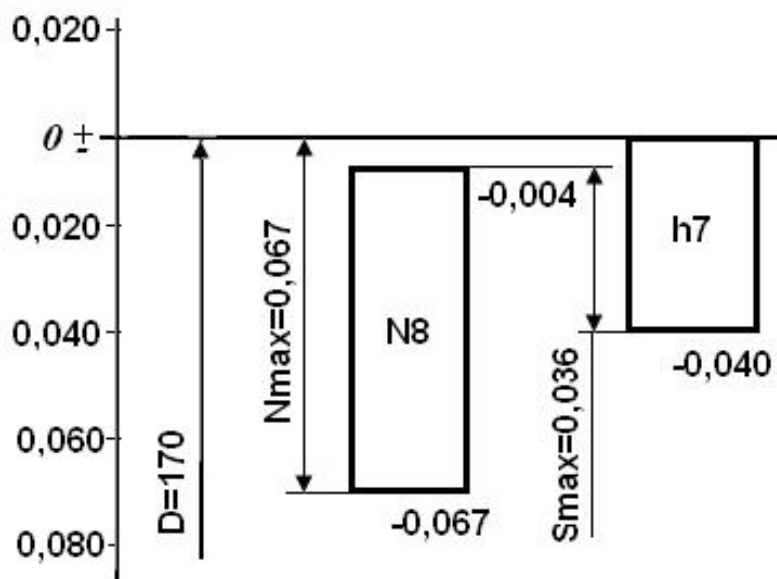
Схема розташування полів допусків деталей з'єднання $\varnothing 170N8/h7$
